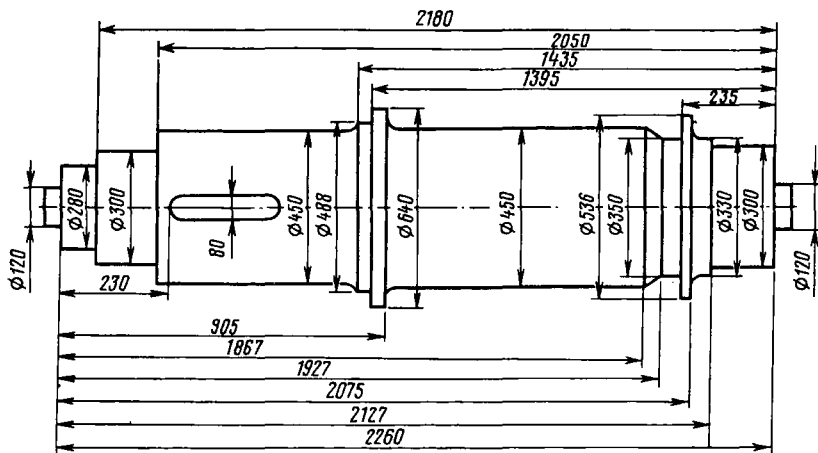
Упрощенный чертёж главного приводного вала эскалатора ЭТ-2
